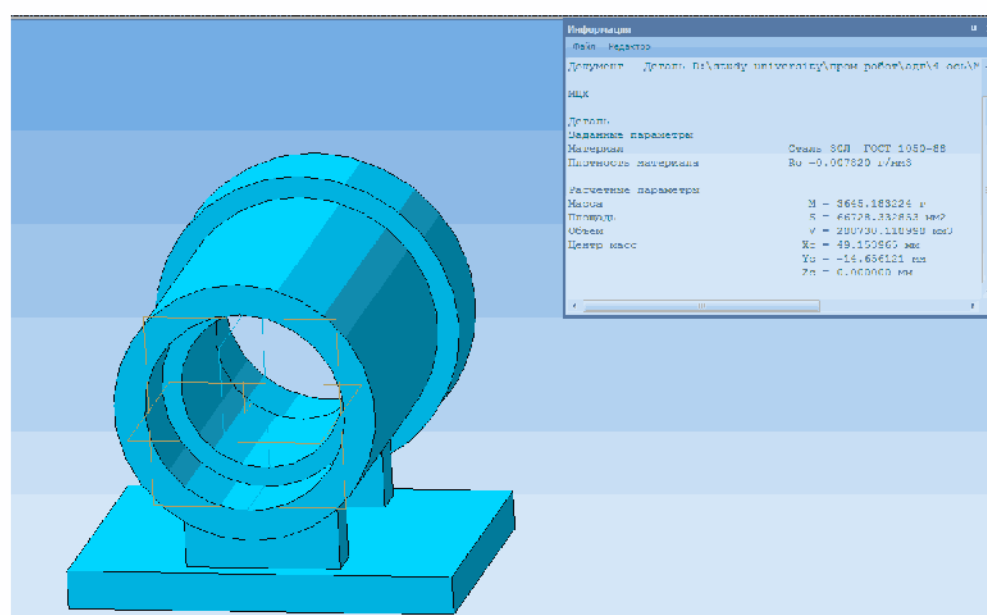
3d модель заготовки при литті в оболонкові форми форми
